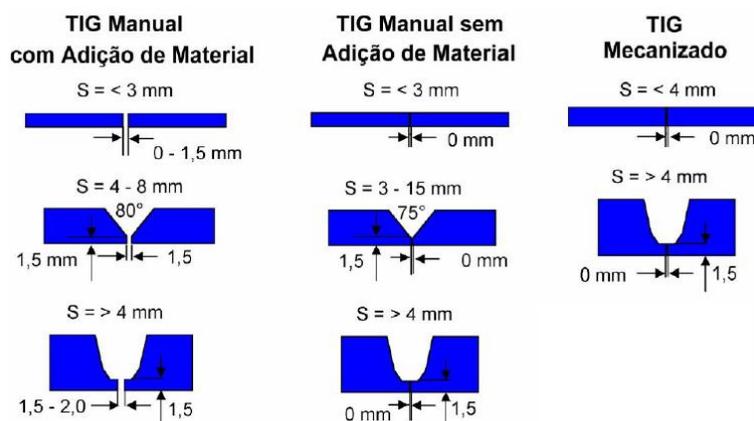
Tipos de Juntas Utilizadas na Soldadura TIG [36]
